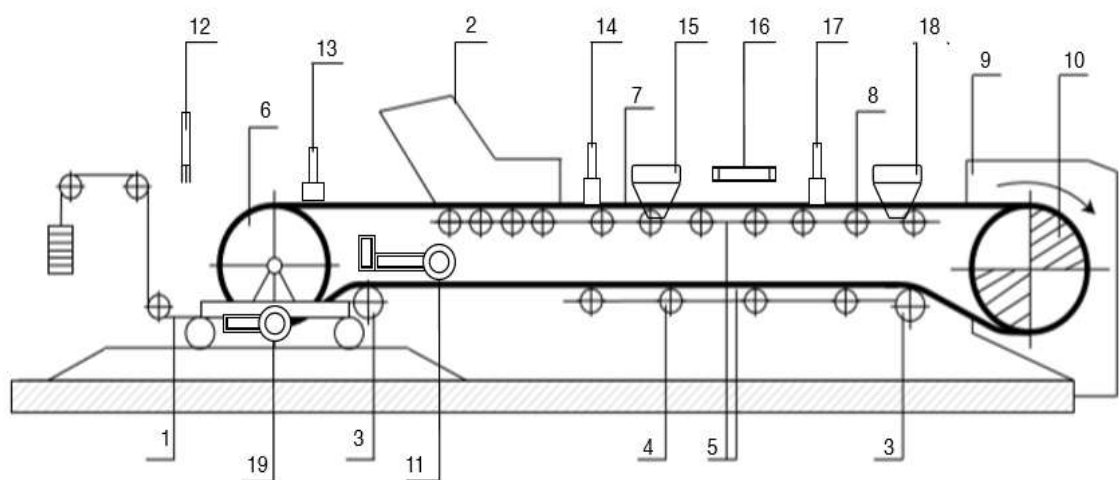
Схема автоматичного керування стрічкового конвеєра
